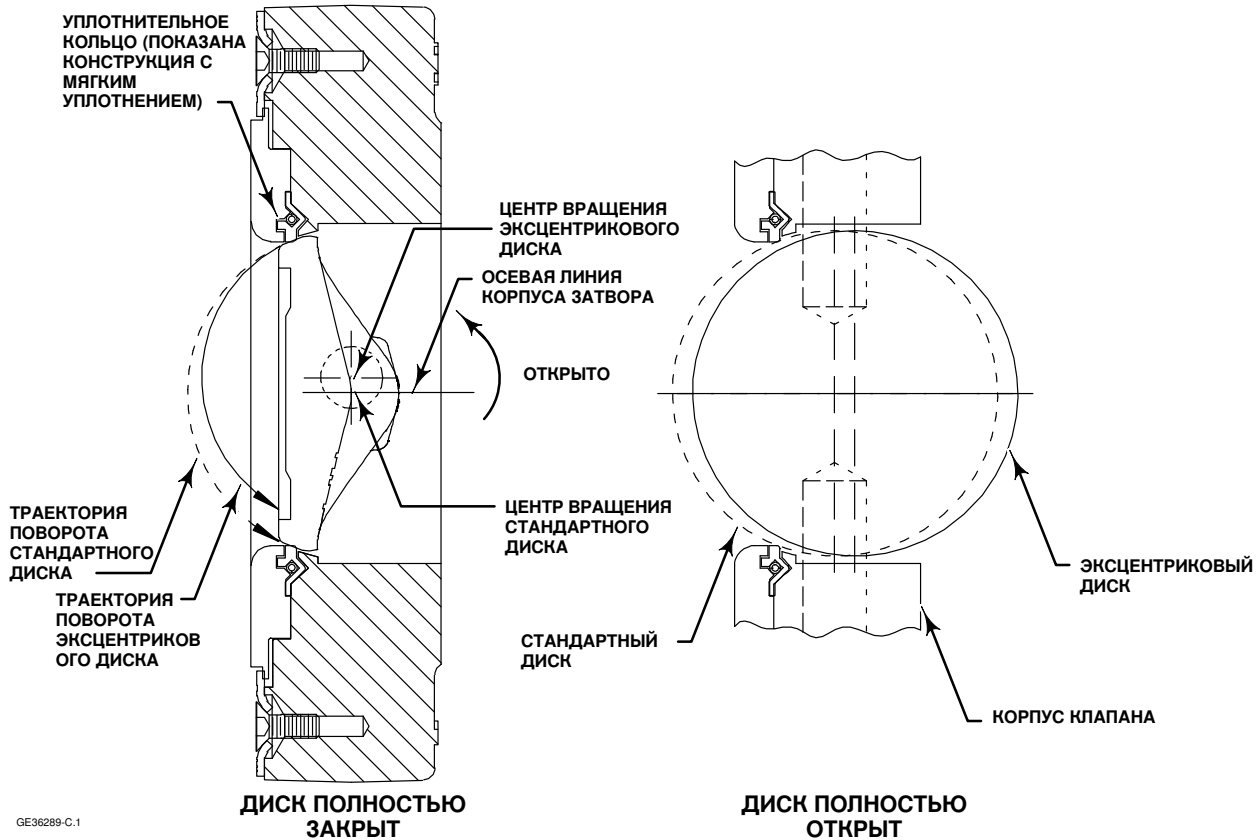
Деталировочный чертеж конструкции типowego затвора Fisher 8580
